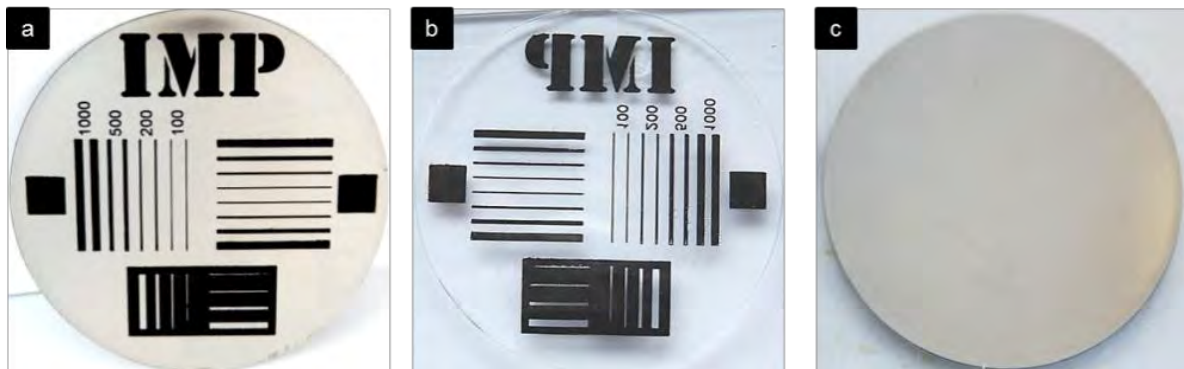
Farbübertrag des Druckmotivs beim In-Mold Printing-Prozess von Polycarbonat: a) Druckbild auf dem Werkzeug, b) In-Mold bedrucktes Polycarbonatteil, c) Werkzeug nach dem Hinterspritzen [Hae13b]
